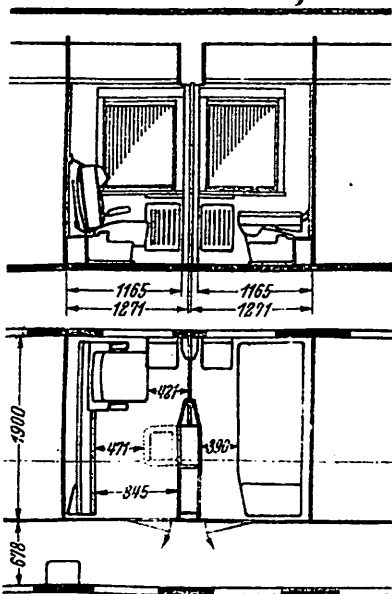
Einstöckiger Typ mit klappbaren Querbetten.
